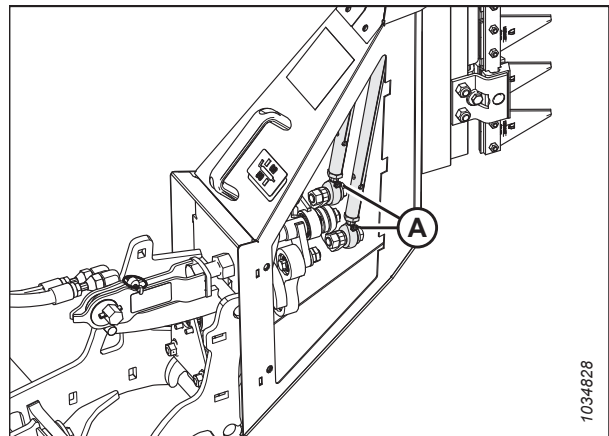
Graissage des embouts sur les tiges-poussoirs des couteaux verticaux
